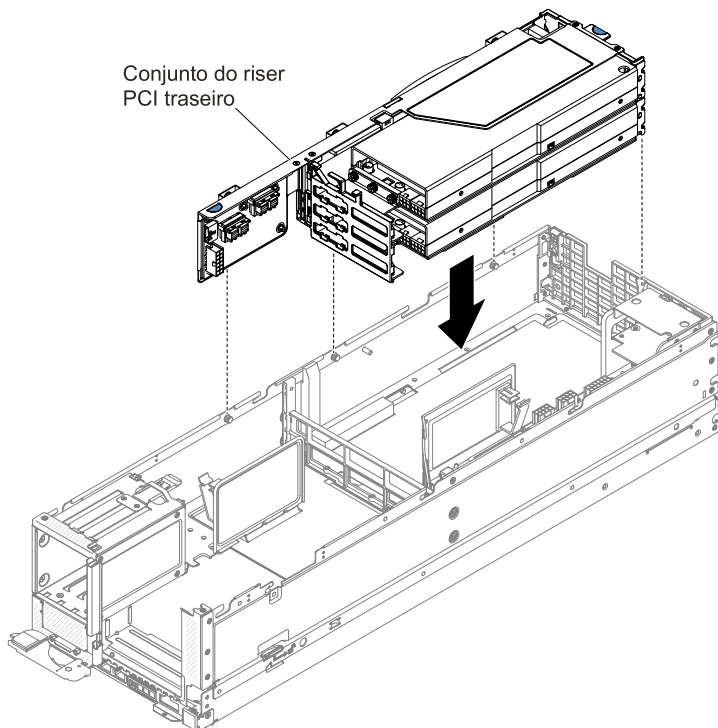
Instalação do conjunto do compartimento da placa riser PCI traseiro
